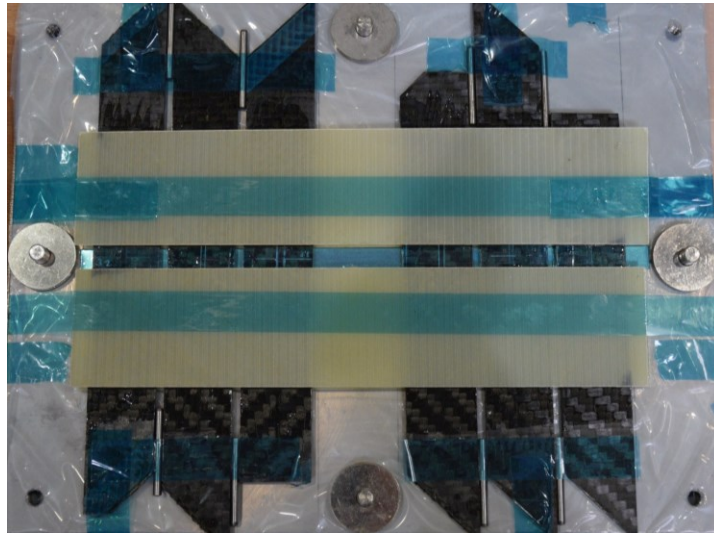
Druck-Lücke 0°-Prüfkörper im Klebewerkzeug
